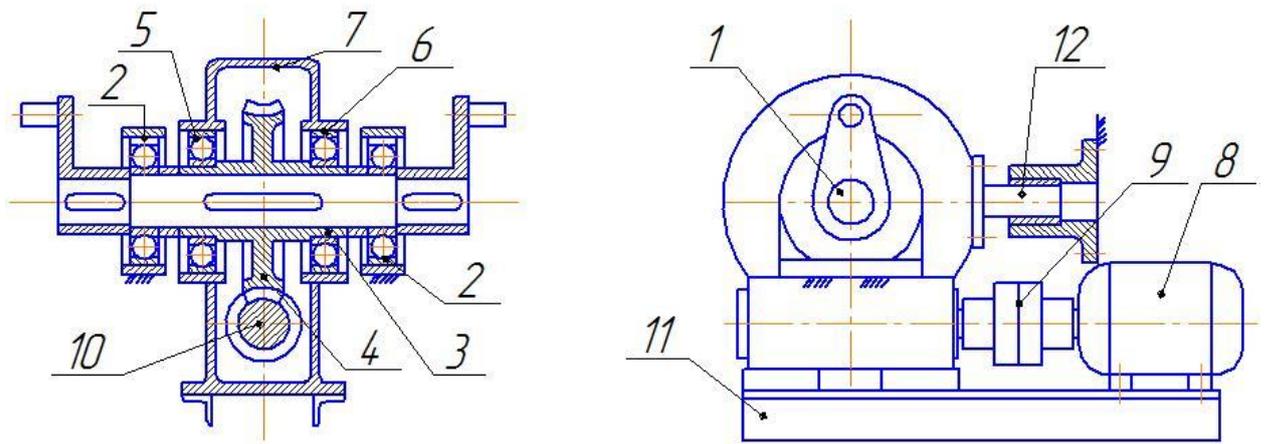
Редуктор с электродвигателем, подвешенным на кривошипном валу в подшипниковых опорах
